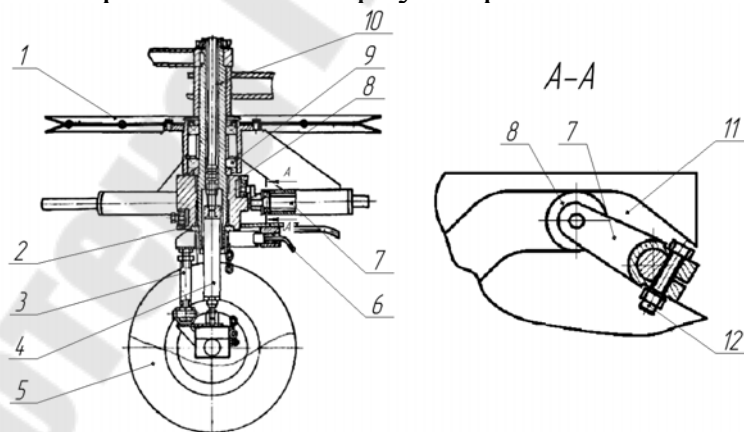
Ротор правый: 1 – шкив; 2 – копир; 3 – упор; 4 – гидроцилиндр; 5 – ход колесный; 6 – фиксатор; 7 – штанга; 8 – ролик; 9 – корпус; 10 – ось; 11 – дорожка копира; 12 – болт
